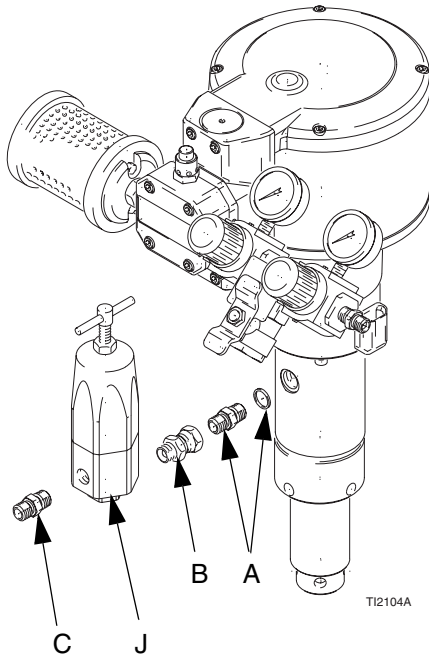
Regulador de fluido en un sistema sin filtro de fluido
